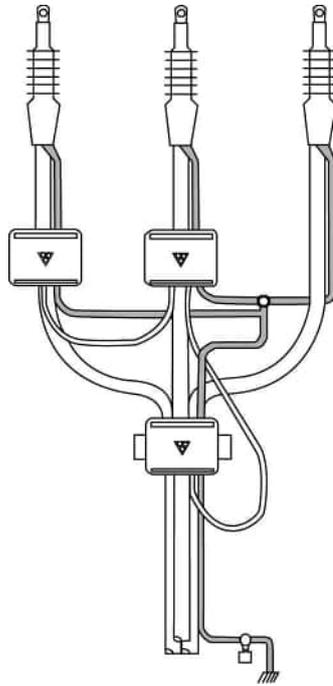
Montaggio dei sensori di cortocircuito e guasto di terra sul cavo
